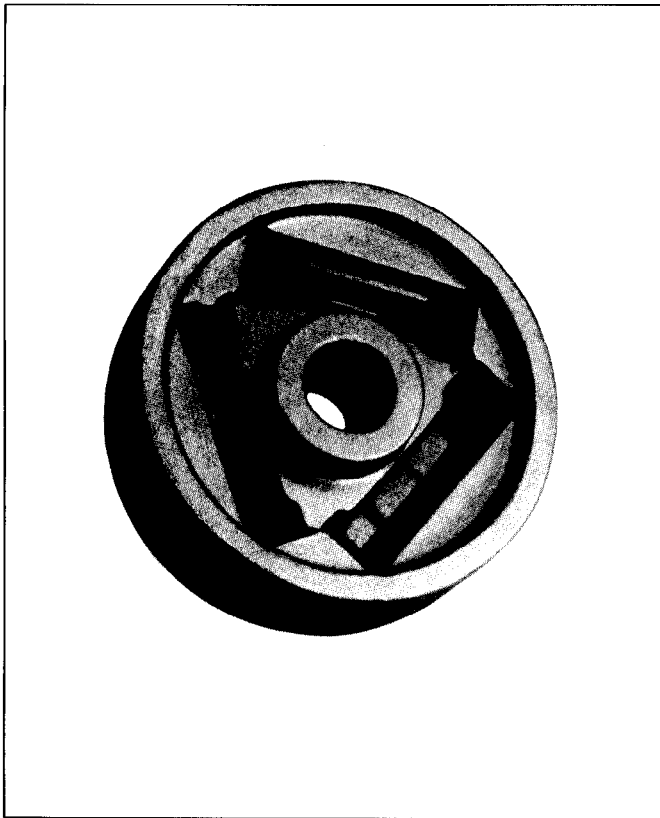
Gesenkgeschmiedeter Futterkörper (33 kg) aus C 45 für Drehmaschinen
